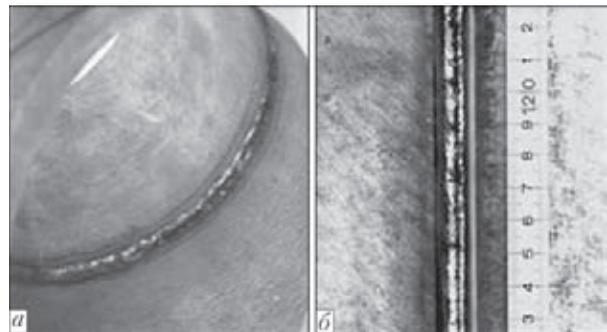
Блестящий гладкий валик на обратной (а) и лицевой (б) поверхности корневого шва (сталь 304, пруток TG-X308L)
